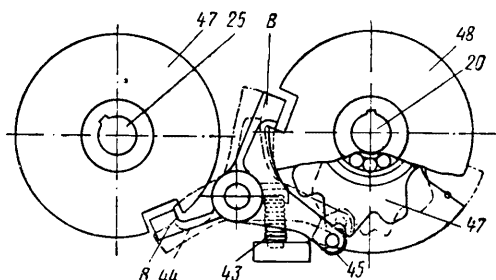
Механическая блокировка между главным, тормозным и реверсивным валами контроллера:
